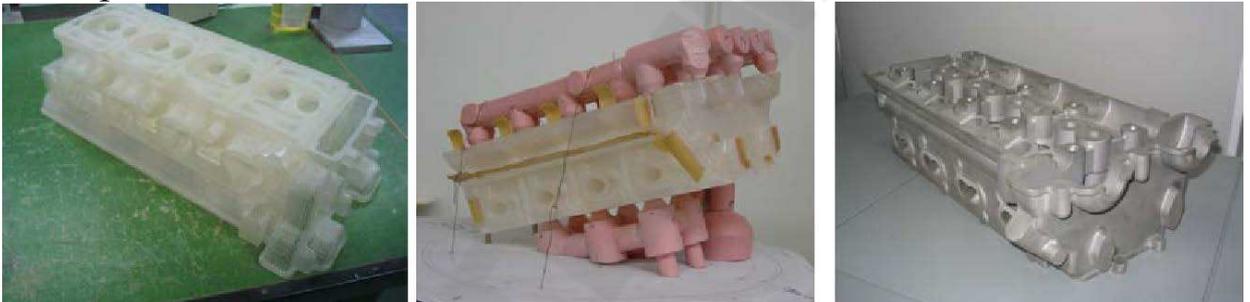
Quick-cast модель, она же с литниковой системой и отливка головки цилиндров (Al)
